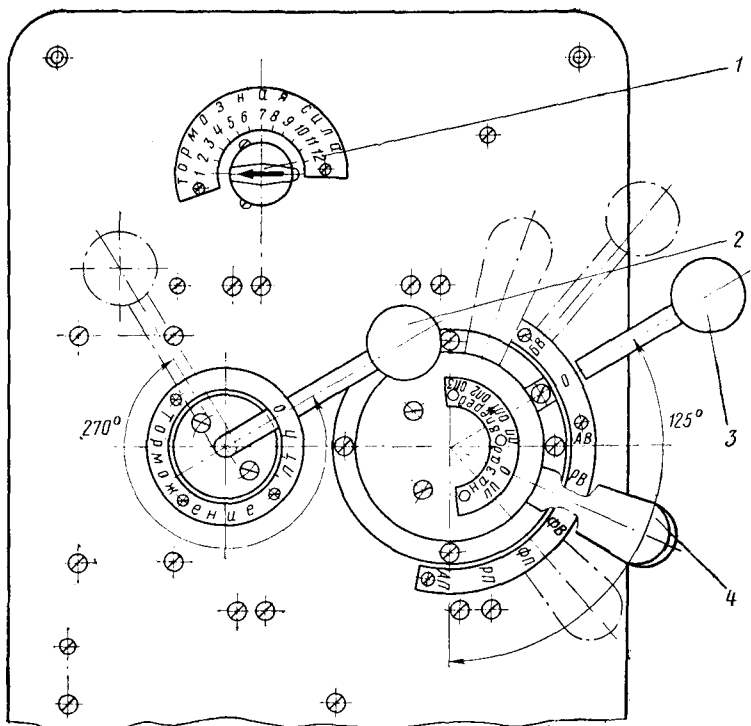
Контроллер машиниста КМЭ-70 (вид сверху)
